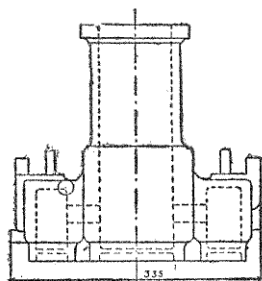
Cylindre double de moteur d'automobile obtenu par moulage mécanique.
